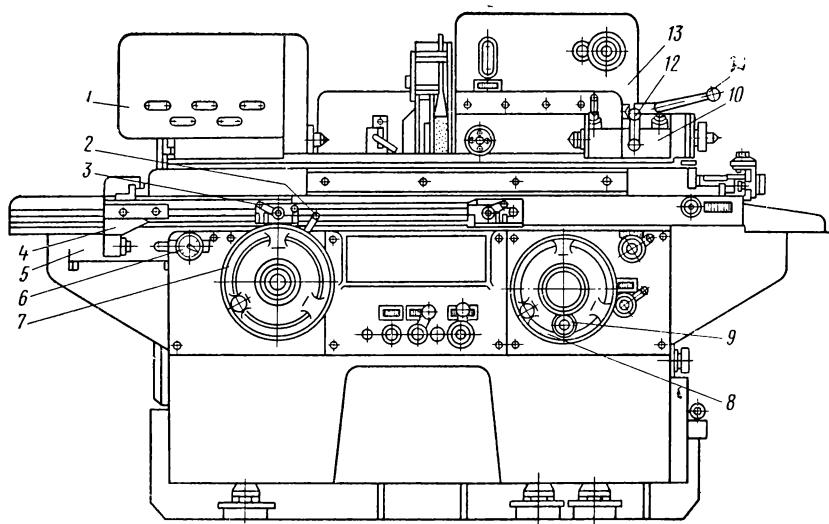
Универсальный круглошлифовальный станок для профильного шлифования:
